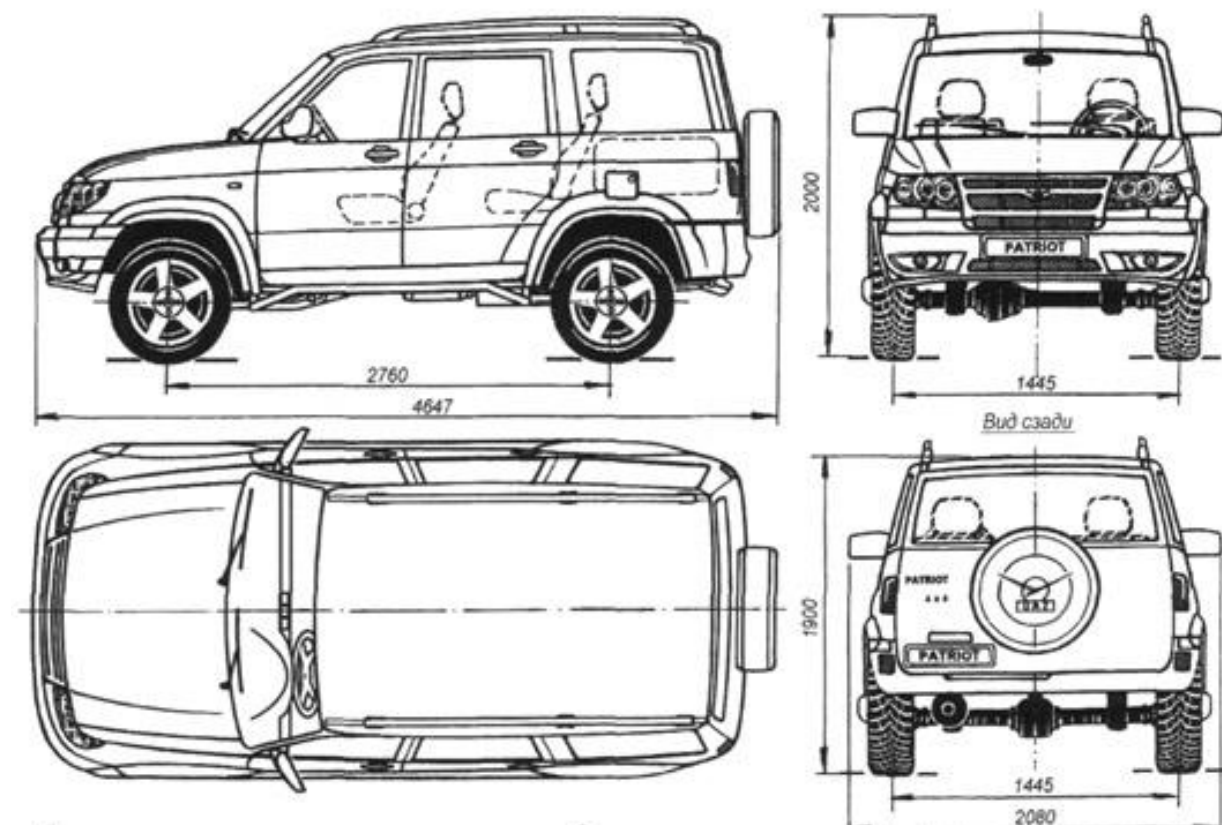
Габаритные размеры автомобиля УАЗ «Патриот».
